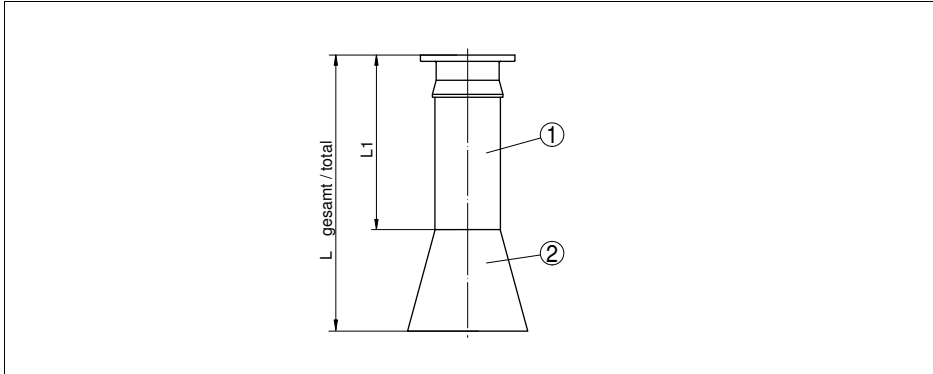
Verlängerung einteilig, mit angeschweißter Hornantenne, Maße je nach Bestellspezifikation
